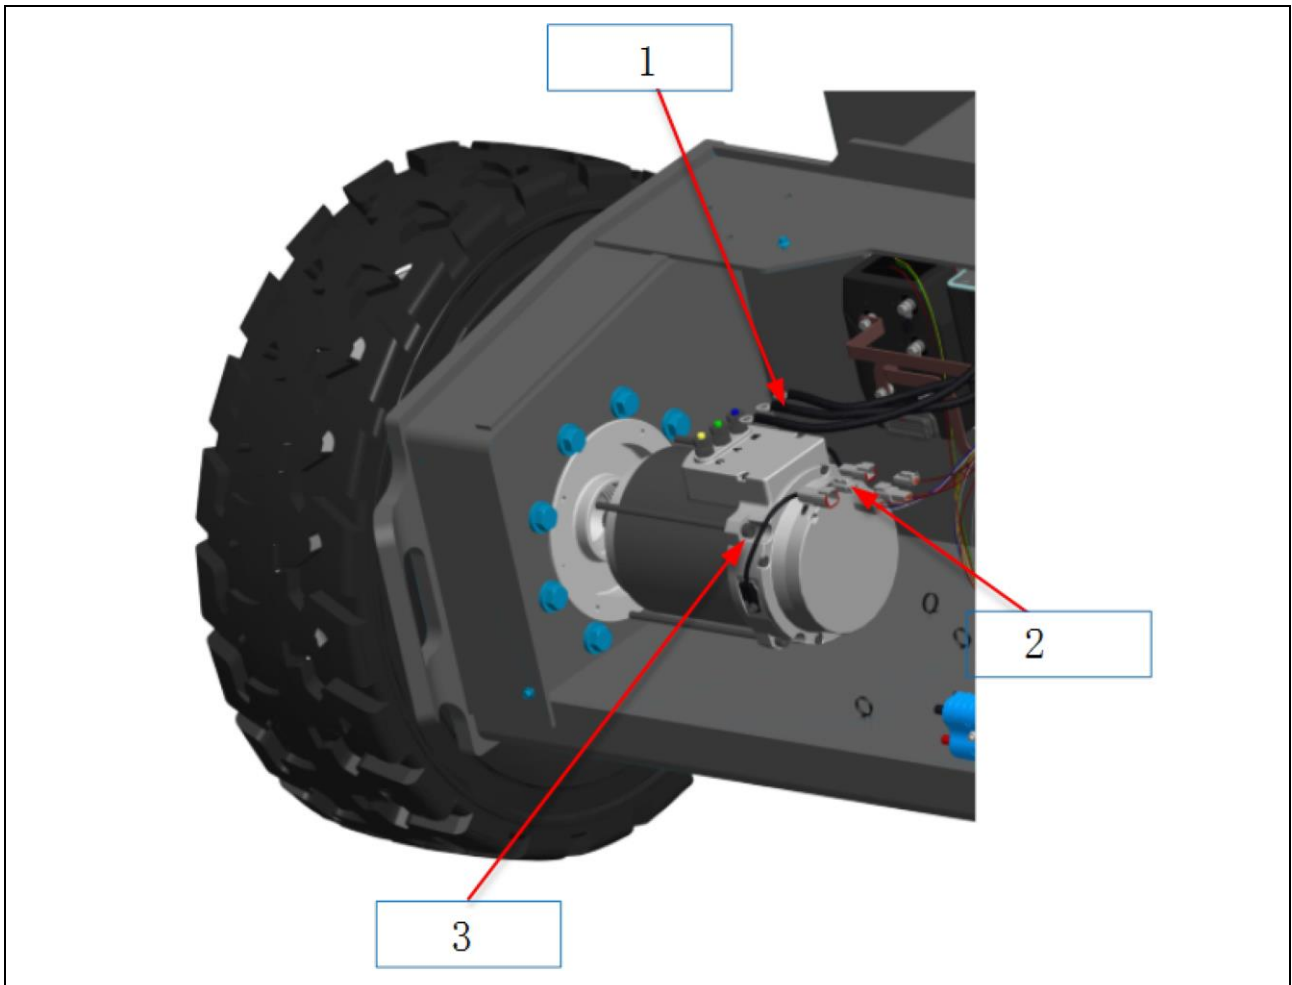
Diagrama esquemático de desmontagem do motor de viagem
